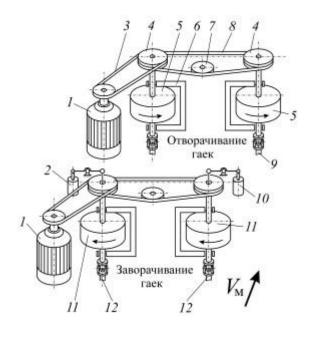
Привод вращения шпинделей гайковертов одного блока: 1 — электродвигатели; 2 и 10 — гидроцилиндры переключения режимов маховика с гидромуфтой; 3 и 8 — ремни клиноременных пе-редач; 4 — шкивы; 5 — маховики; 6 — рама бока; 7 — натяжные шкивы; 9 и 12 — карданные валы; 11 — маховики со встроенными переклю-чаемыми гидромуфтами
